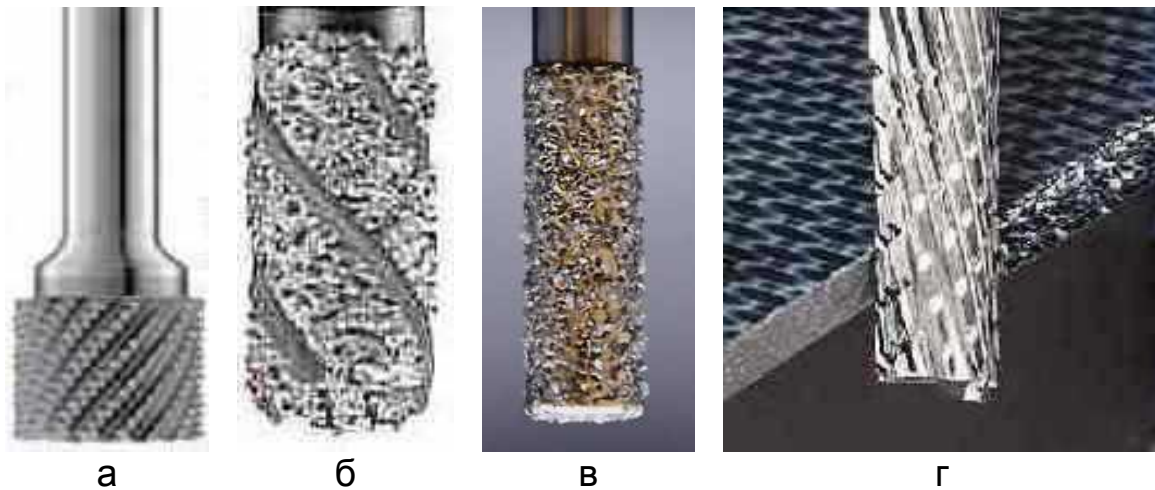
Кінцеві фрези з алмазною кулькою для видів обробки: а – чорновий; б – напівчистовий; в – чистовий; г – приклад фрезерування композитної обшивки
